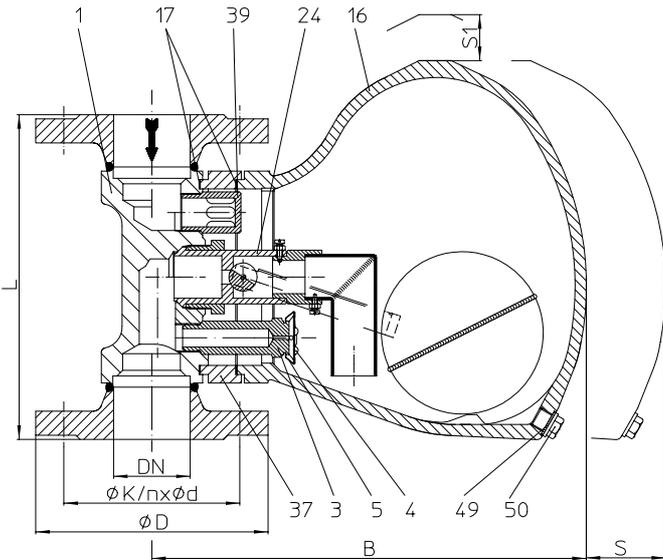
1 mit Flanschen - vertikale Einbaulage
